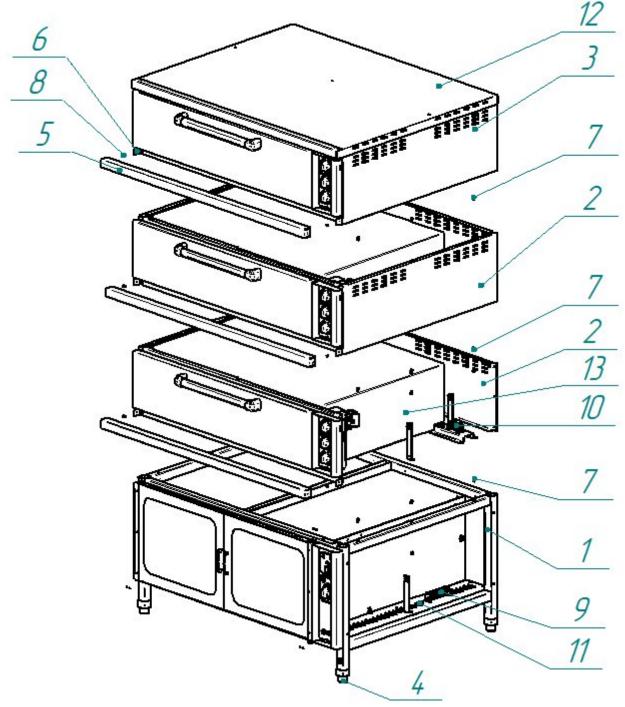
Схема сборки шкафа ШРТ 4-ЭШ + ЭШ-3К
